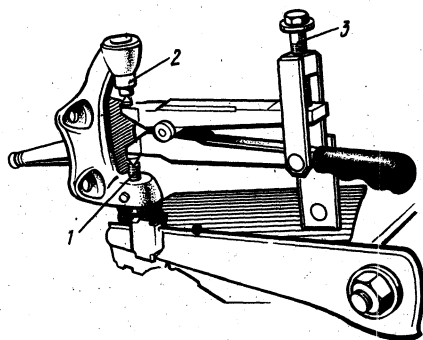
Выпрессовка пальца нижнего шарового шарнира автомобиля «Жигули»:
